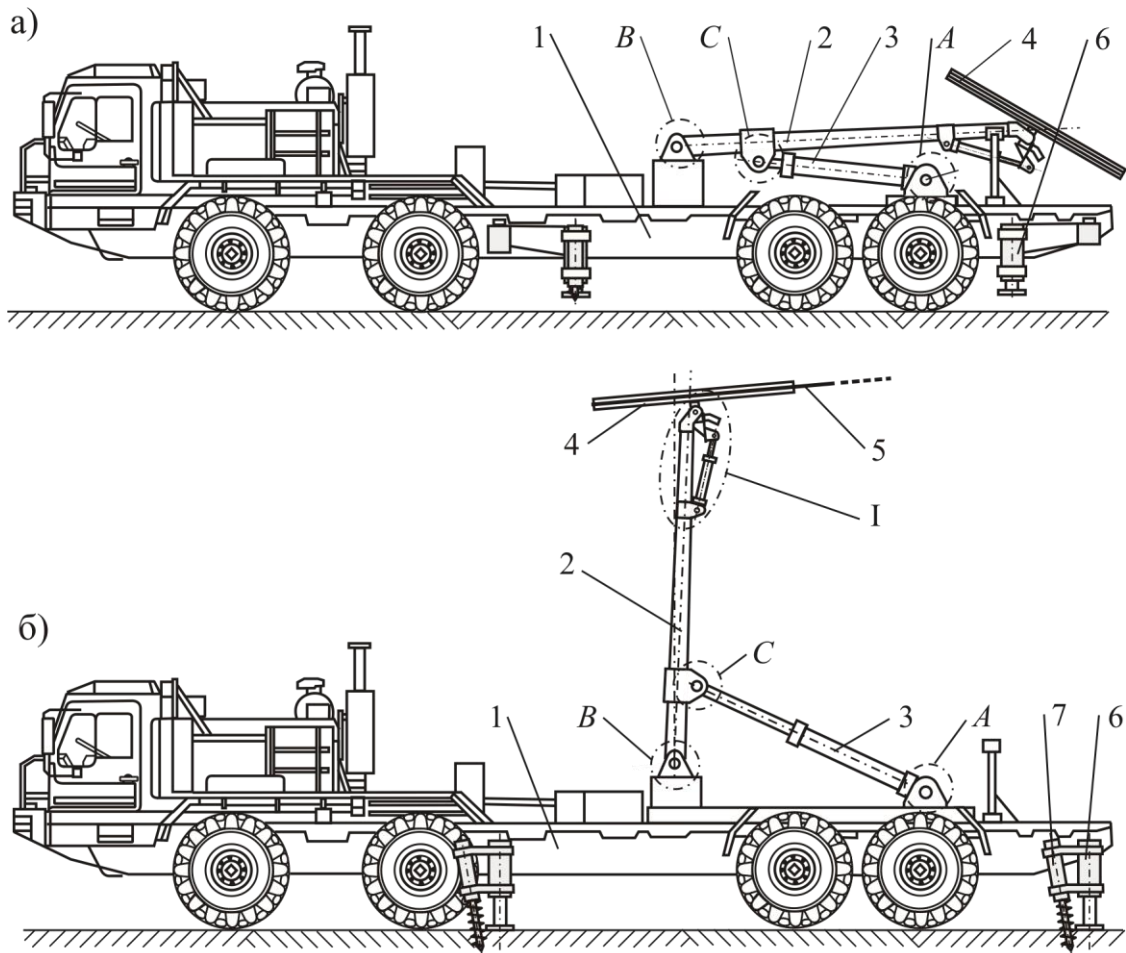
Общий вид концевой базовой станции (вид сбоку) с центральным расположением опоры при опирании на несущую раму шасси [10, 11]: а - транспортное положение концевой опоры; б - рабочее положение концевой опоры (1 – несущая рама базового шасси; 2 – концевая опора; 3 – подъемный гидроцилиндр; 4 – канатный шкив; 5 – несуще-тяговый канат; 6 – аутригер; 7 – анкерное устройство; А – шарнир крепления гидроцилиндра к надрамной конструкции шасси; В – шарнир крепления концевой опоры к надрамной конструкции шасси; С – шарнир крепления концевой опоры и подъемного гидроцилиндра; I – механизм привода и пространственной ориентации канатного шкива)
